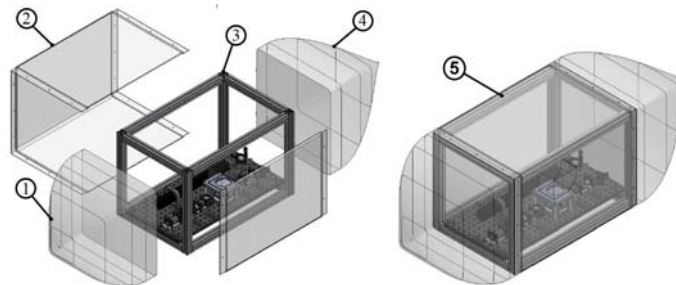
Partes de la canastilla: 1) parte frontal, 2) sección intermedia, 3) estructura metálica, 4) sección trasera, y 5) ensamble de la canastilla.
